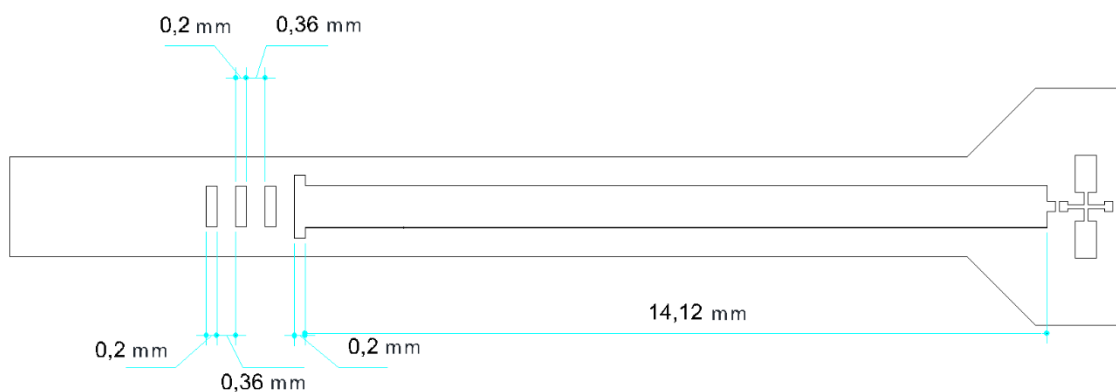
Detalle del diseño de la estructura en AutoCAD.
